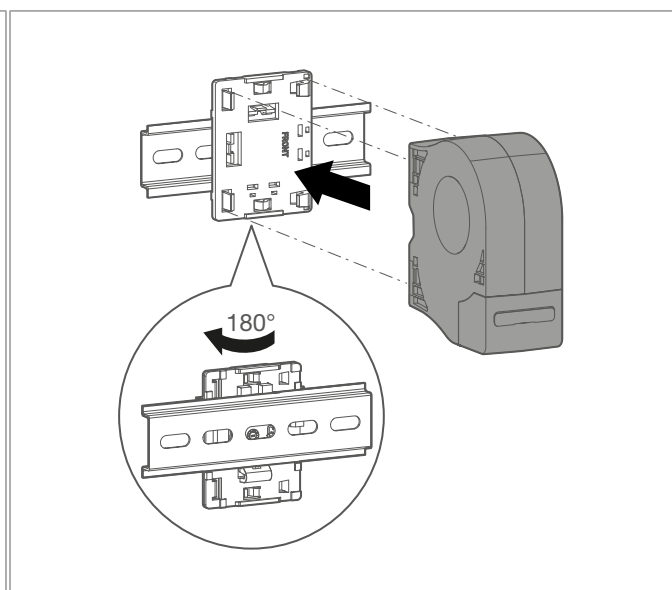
HR72x - Montage horizontal sur le rail DIN
